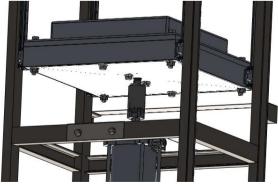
i: Detalle de fijacion placa inferior
